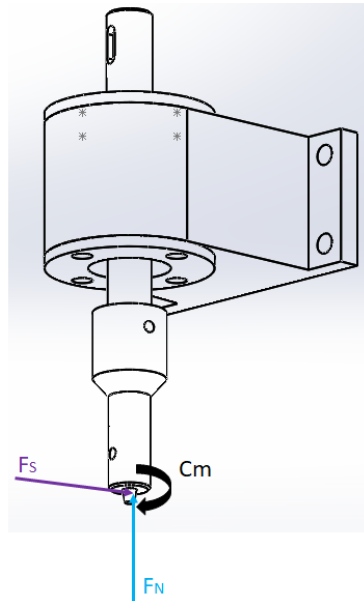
Schéma des forces appliquées sur l'outil et le porte-outil.
